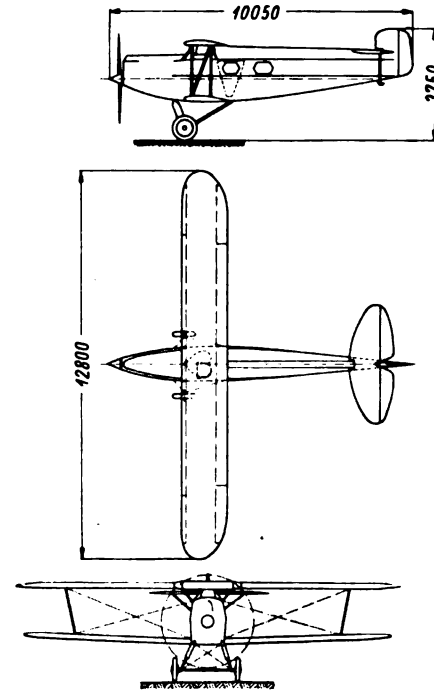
Zusammenstellungszeichnung des Flugzeuges.
